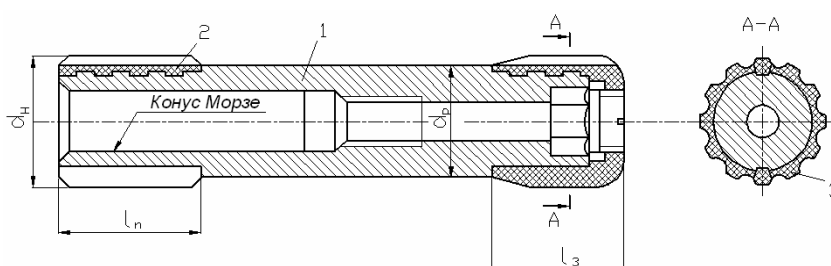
Конструкция электрода-инструмента для обработки внутренних поверхностей круглых труб:
